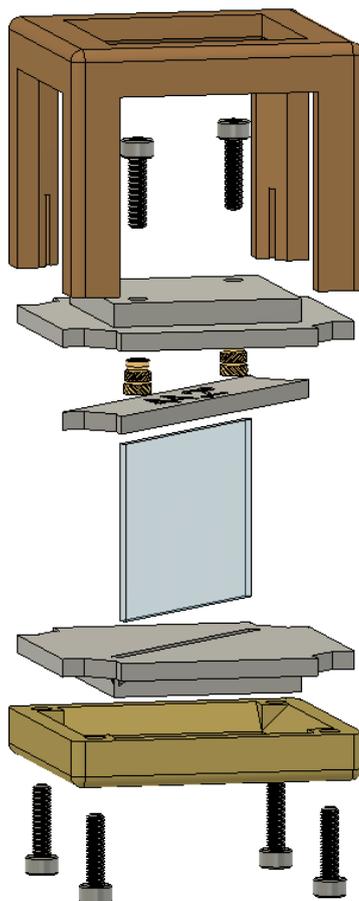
Explosionsansicht des Strahlteiler-Würfels
